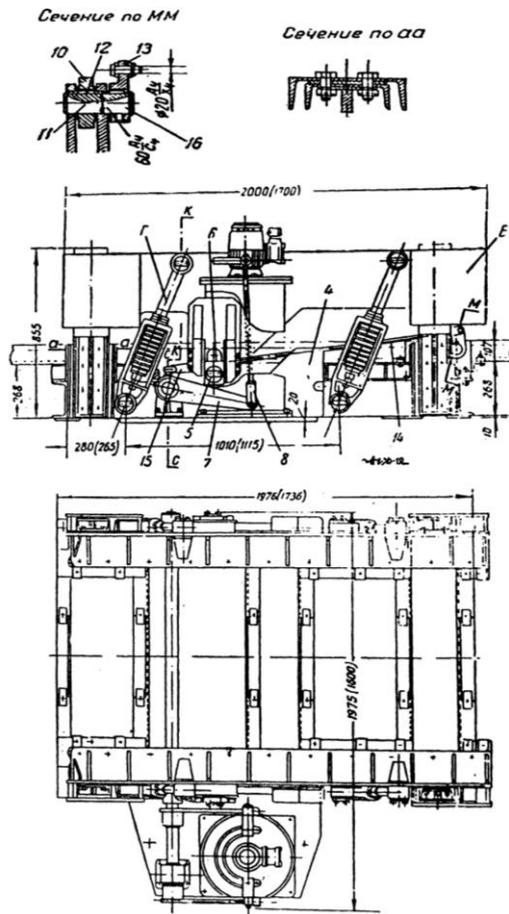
Путьевые тормоза ПТ-5 и ПТ-6: А – рама; Б – электрогидравлический привод; В – тормозные лыжи; Г – амортизатор; Д – приводной вал; Е – подставка для рельсов
